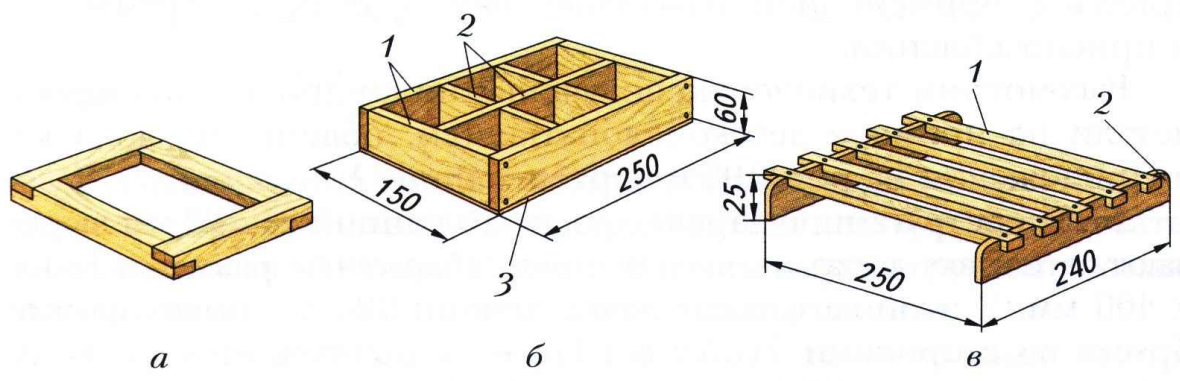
Изделия из древесины: *а* – рамка; *б* – коробка для мелких деталей: 1 – стенки; 2 – перегородки (фанера); 3 – дно (фанера); *в* – подставка для цветочного горшка: 1 – планка; 2 – опора
